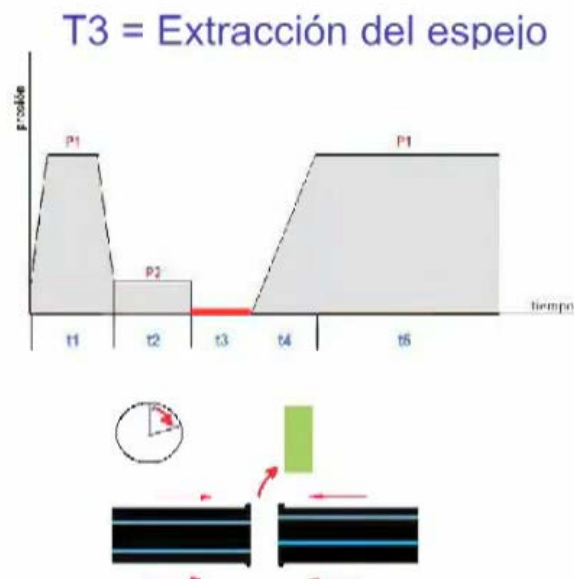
esquema del proceso de soldadura. Extracción del espejo.
